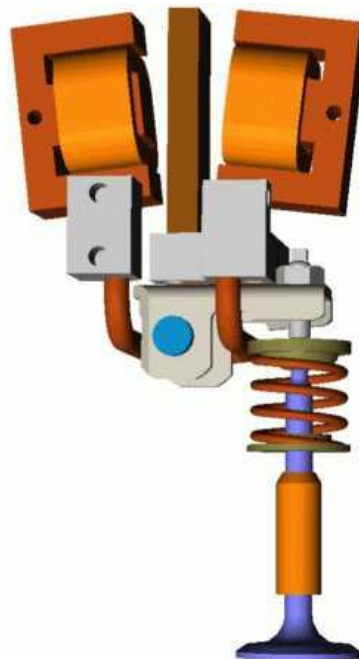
Elektro-hydraulické ovládání ventilů [3]
